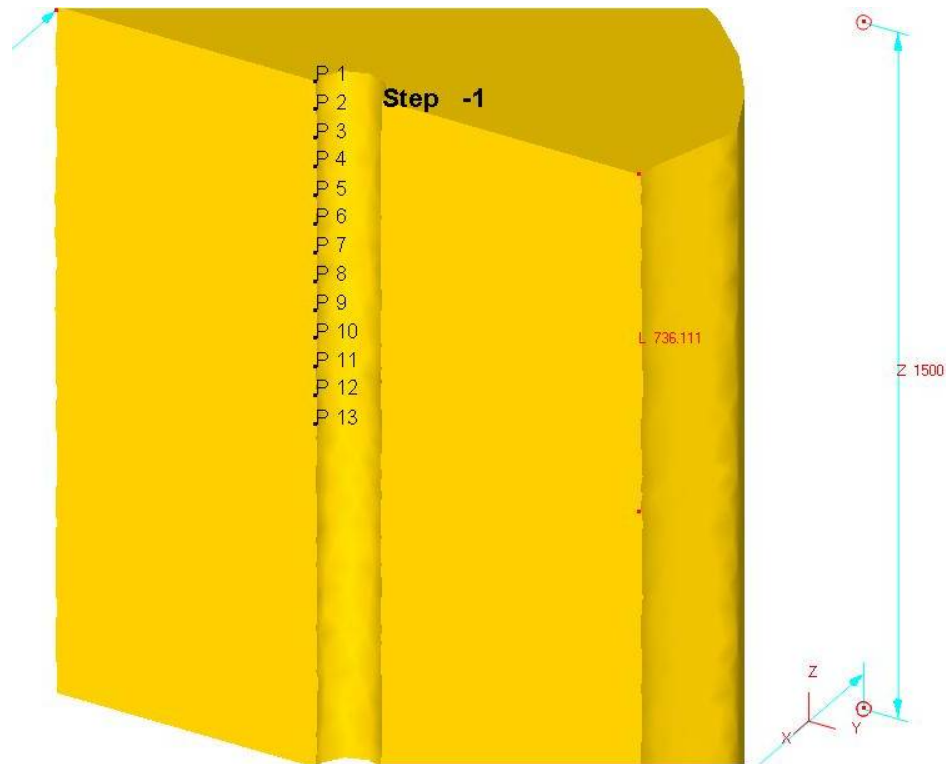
Расстановка контрольных точек на границе дефекта до осадки четырёхлучевой заготовки
